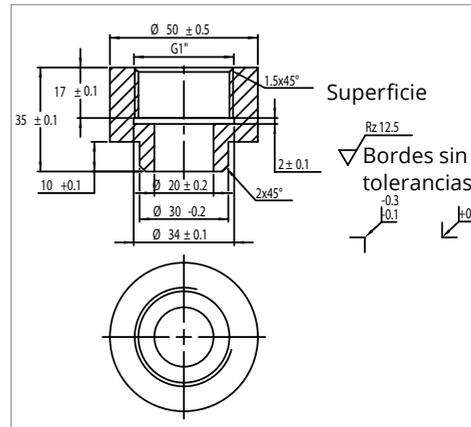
Adaptador soldado en la tubería de entrada
